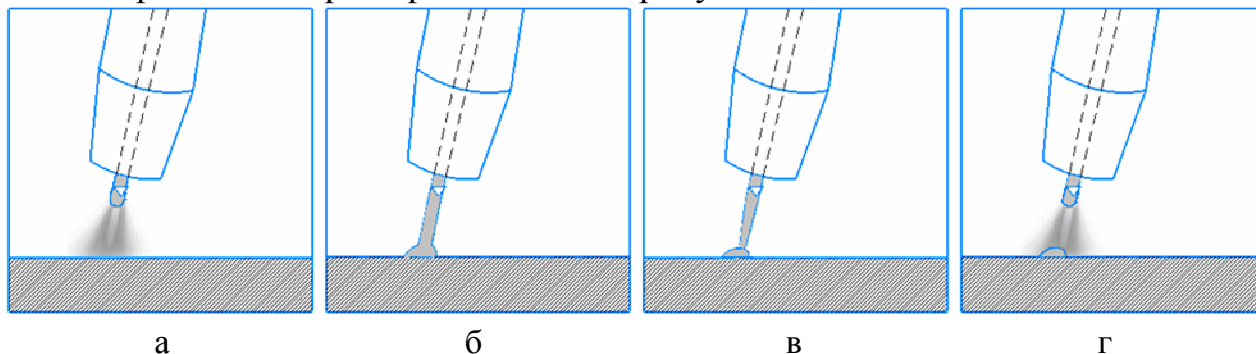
Процесс переноса металла при СМТ сварке: а, б, г – движение проволоки в зону горения дуги; в – реверсивное движение
